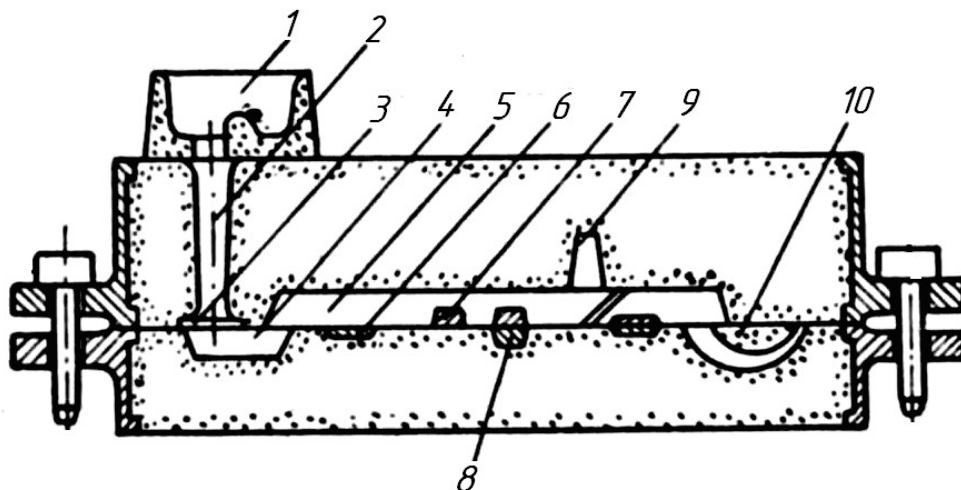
Схема литниковой системы: 1 – литниковая чаша; 2 – стояк; 3 – сетка; 4 – металлоприемник (шлакоуловитель); 5 – коллектор (главный канал); 6 – питатель в нижней опоке (щелевой или ленточный); 7 – толстый питатель в верхней опоке; 8 – питатель в обеих опоках; 9 – шлаковый выпор; 10 – рожковый питатель
